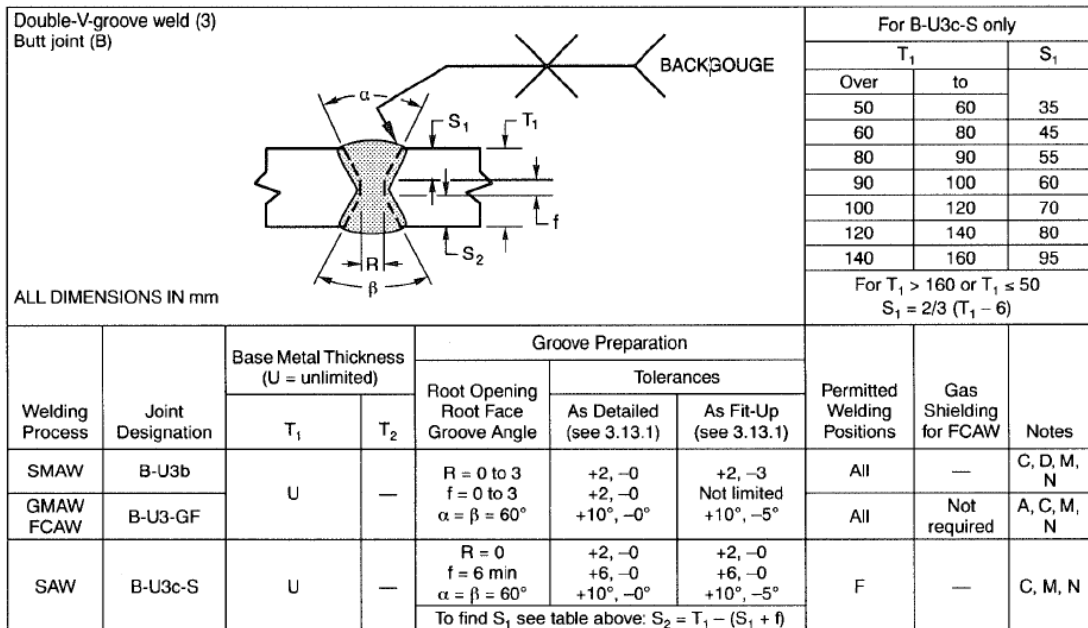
Soldadura Tipo doble V, a tope
